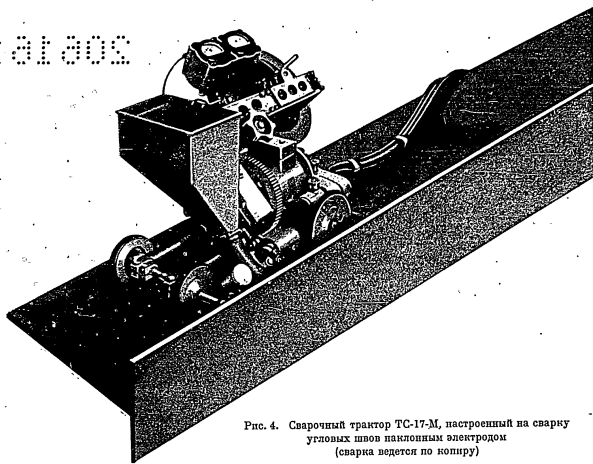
Сварочный трактор ТС-17-М, настроенный на сварку угловых швов наклонным электродом (сварка ведется по копирке)
